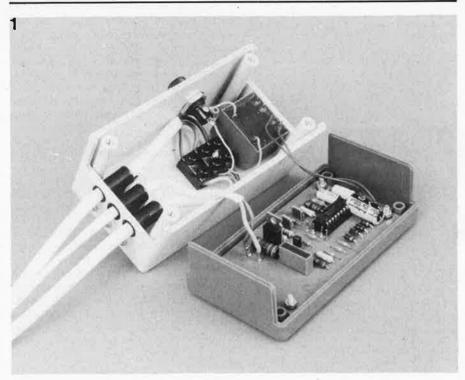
Le circuit imprimé trouve sa place, au millimètre près, dans un boîtier de dimensions 65 x 65 x 120 mm. Il faut utiliser des boulons et des écrous en plastique pour fixer le circuit imprimé, le transformateur et le domino, de manière à garantir une parfaite isolation du courant secteur qui se trouve sur le montage. Il reste également la possibilité de coller le transformateur et le domino sur le boîtier.
